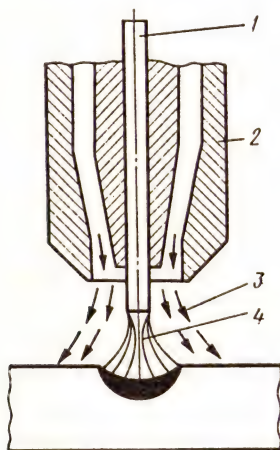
Схема процесса сварки в защитной среде углекислого газа:
